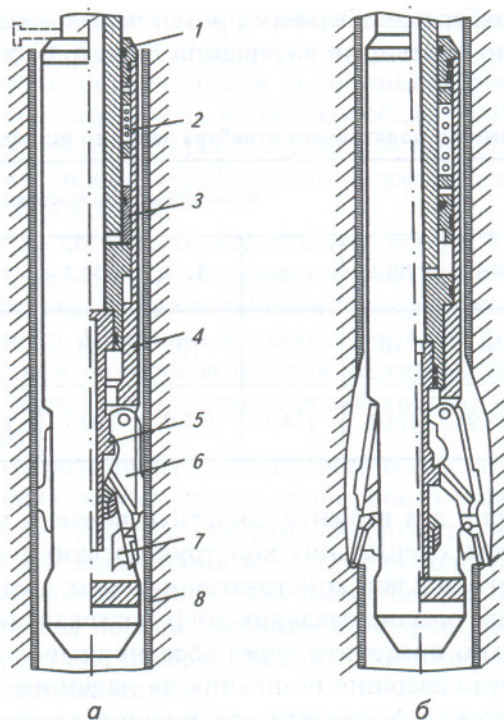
Схема секційного фрезера А. Kammerer в транспортному (а) і робочому (б) станах: 1—шпиндель; 2—пружина; 3—втулка; 4—корпус; 5—клин; 6—лапа; 7—різець; 8—обсадна колона
